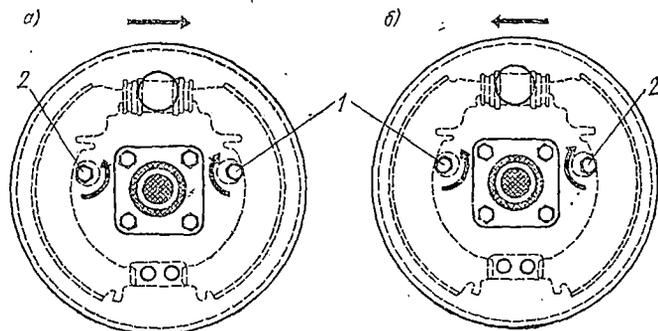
Схема регулировки зазоров между колодками и тормозными барабанами левого (а) и правого (б) задних колес (стрелками показано направление движения автомобиля)
